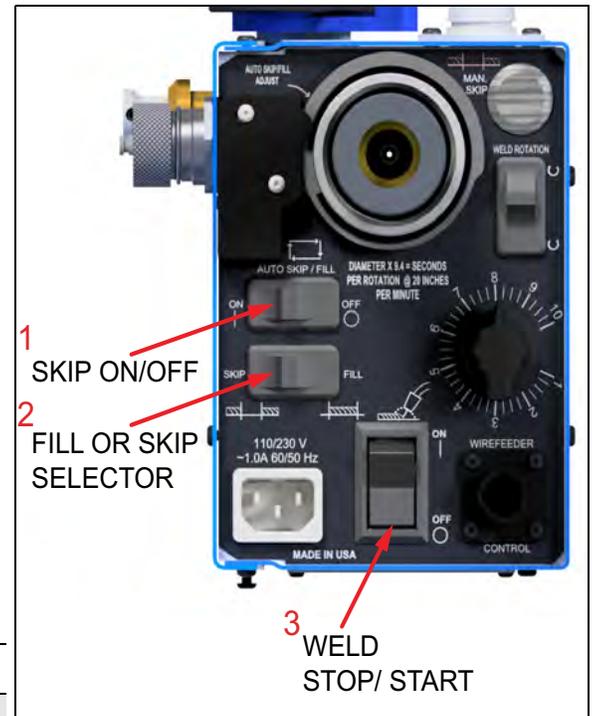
COMMANDES SKIP OU FILL DE LA BW2600
